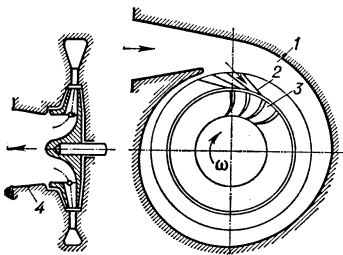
Схема центробежного реактивного турбодетандера: 1—спиральный подвод газа; 2—направляющий сопловой аппарат; 3—ротор; 4—отводной диффузор.
